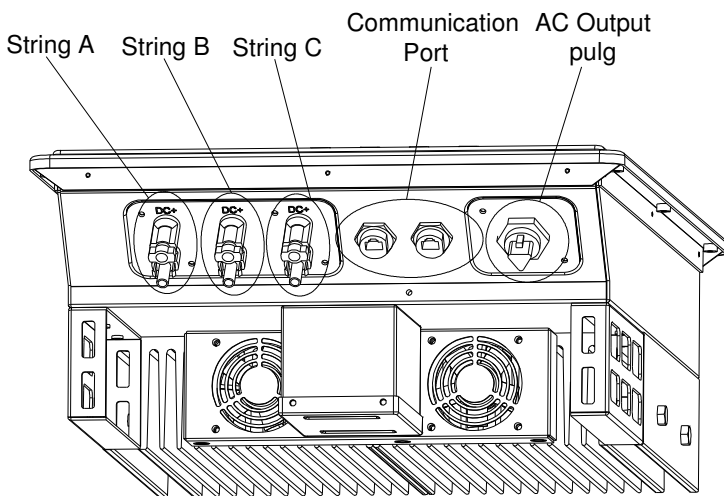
Vista lato inferiore del lato dei collegamenti elettrici
